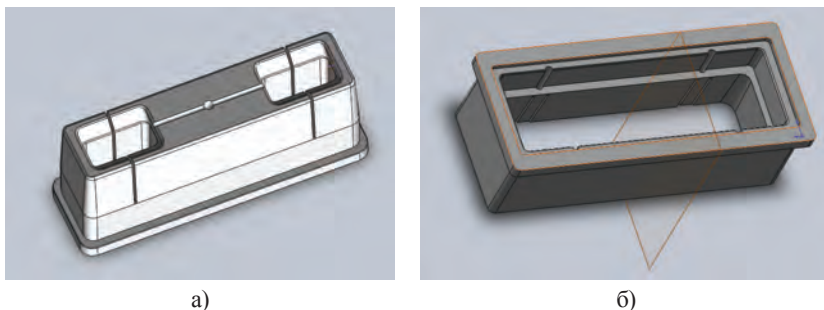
Формообразующие элементы пресс - формы: а – пуансон; б – матрица
